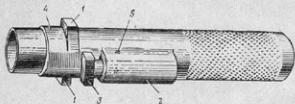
Направляющая трубка возвратно-боевой пружины:
